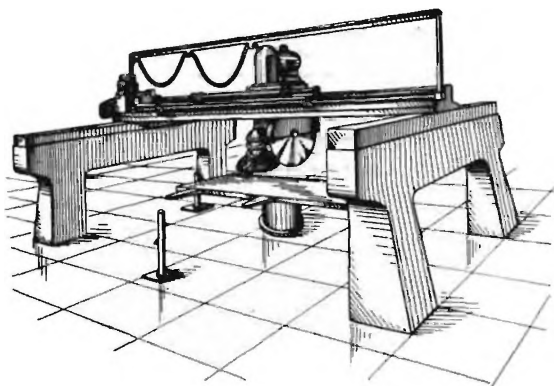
Фрезерно-окантовочный мостовой станок модели ВЖ фирмы «Грегори»
